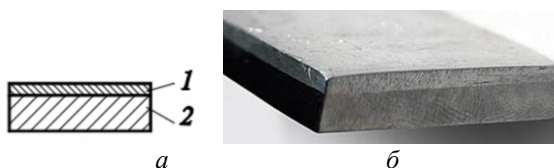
Двошарова біметалева заготовка: *а* – схема складання біметалевої заготовки в пакет (1 - основний шар; 2 – плакуючий шар); *б* – продеформована біметалева заготовка
